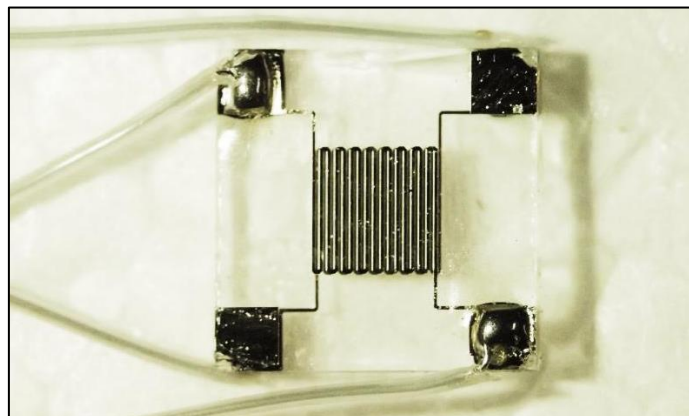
Assemblage par soudure à l'étain
